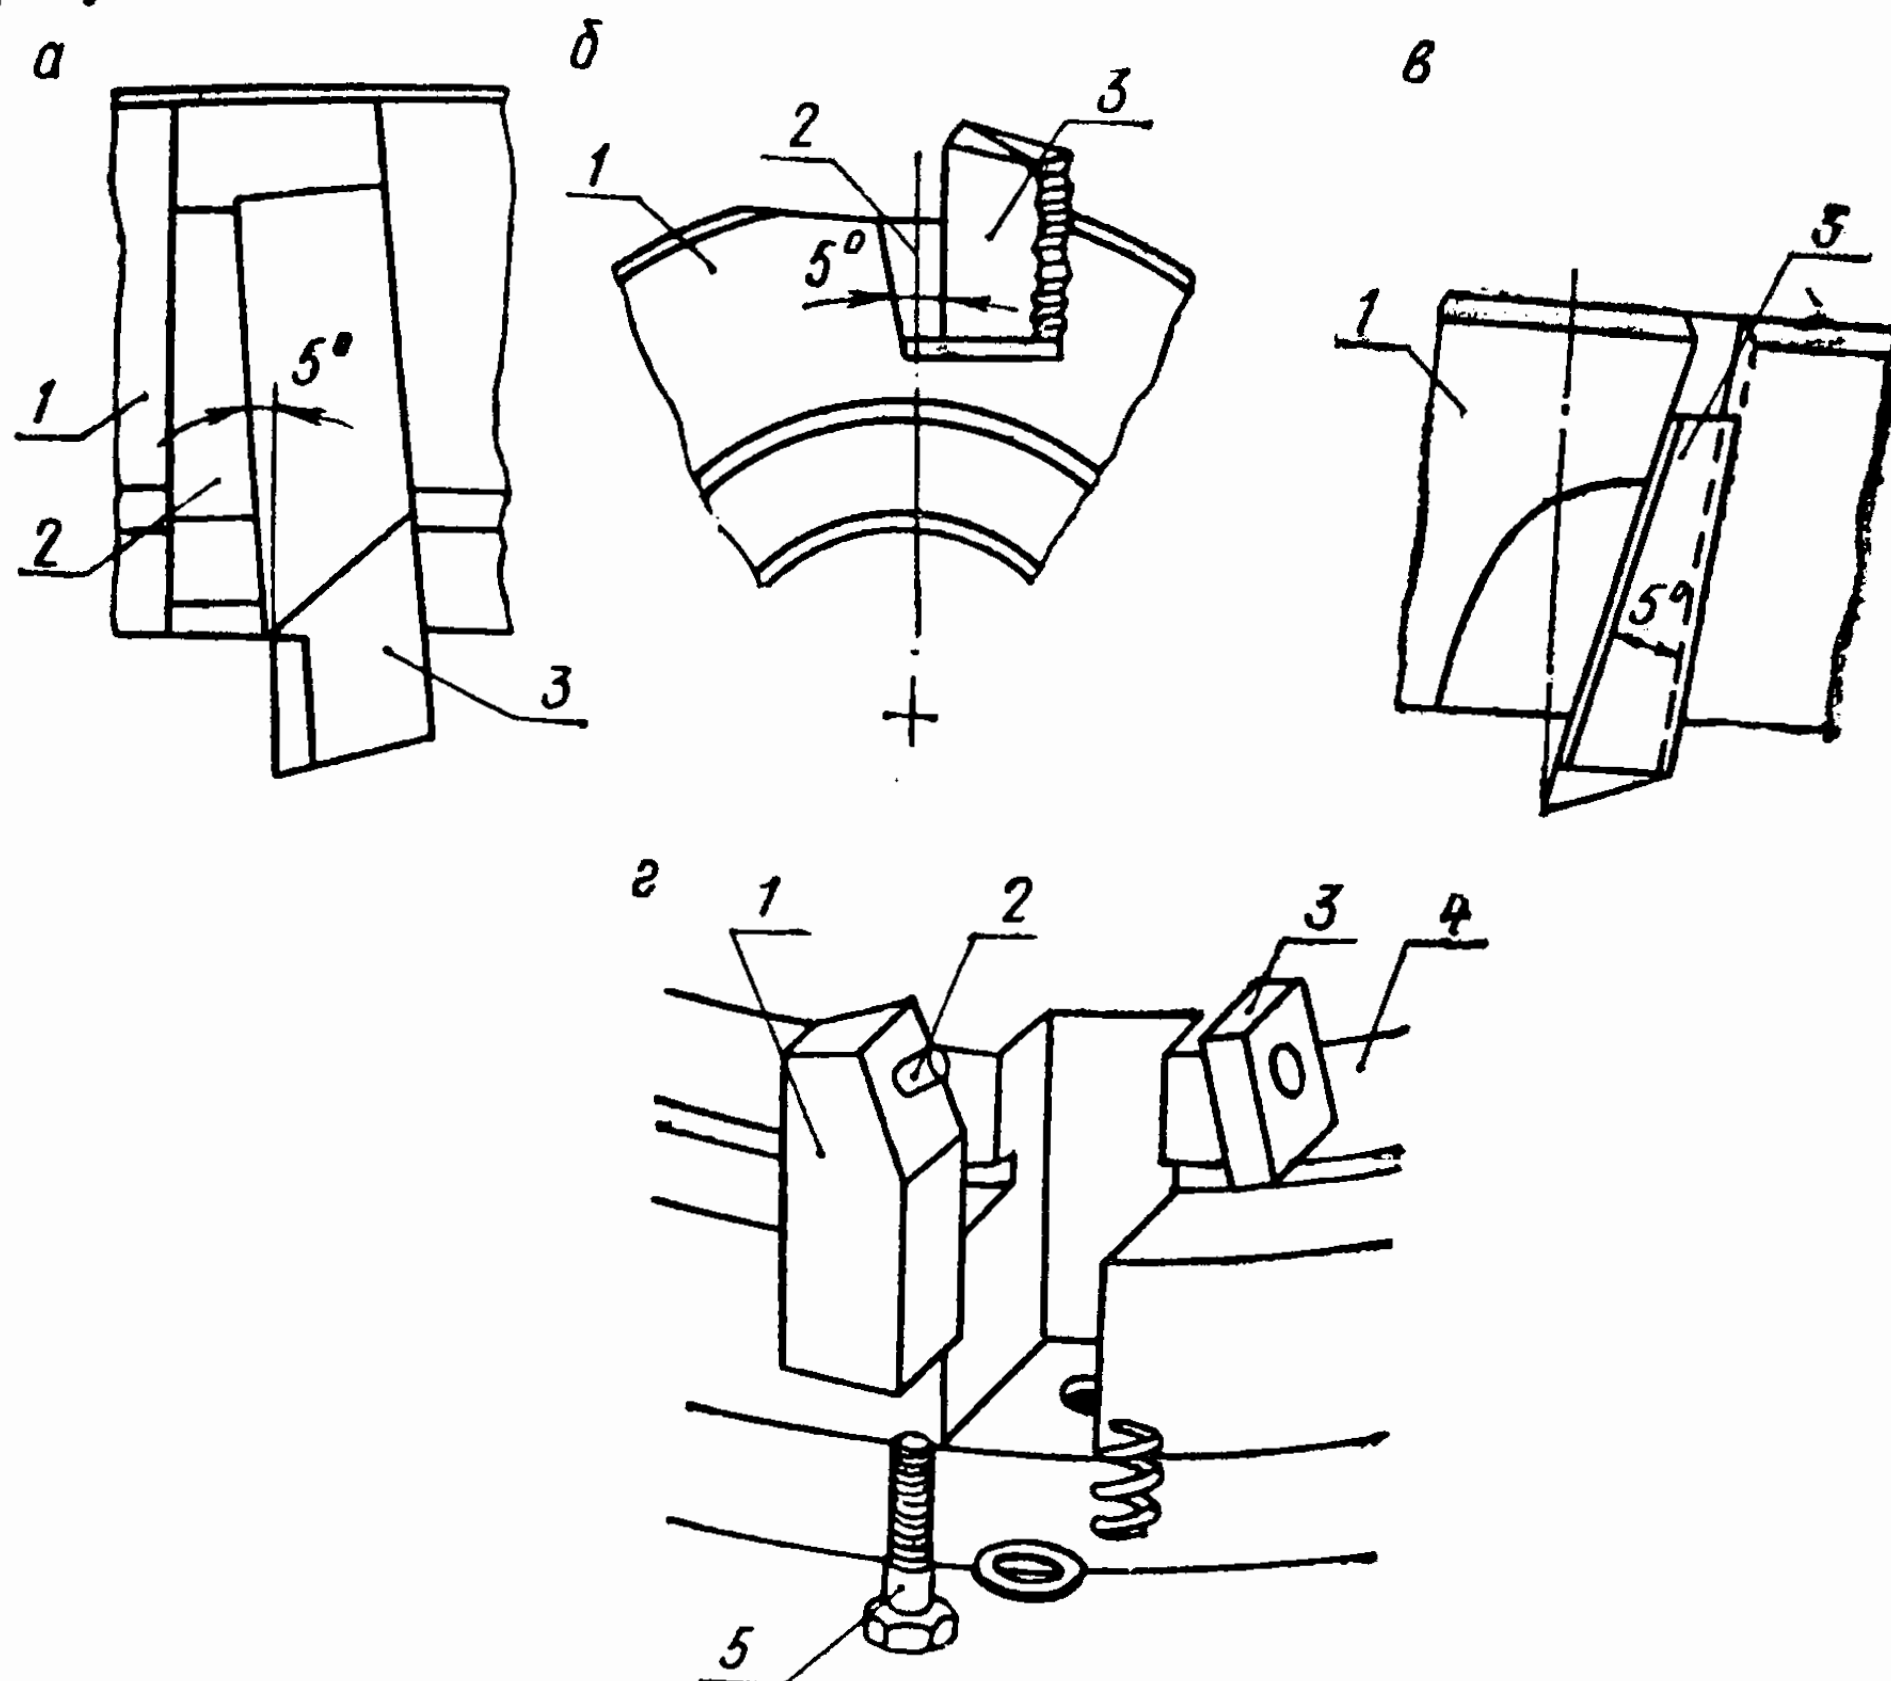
Способы закрепления ножей в корпусе сборных фрез.
